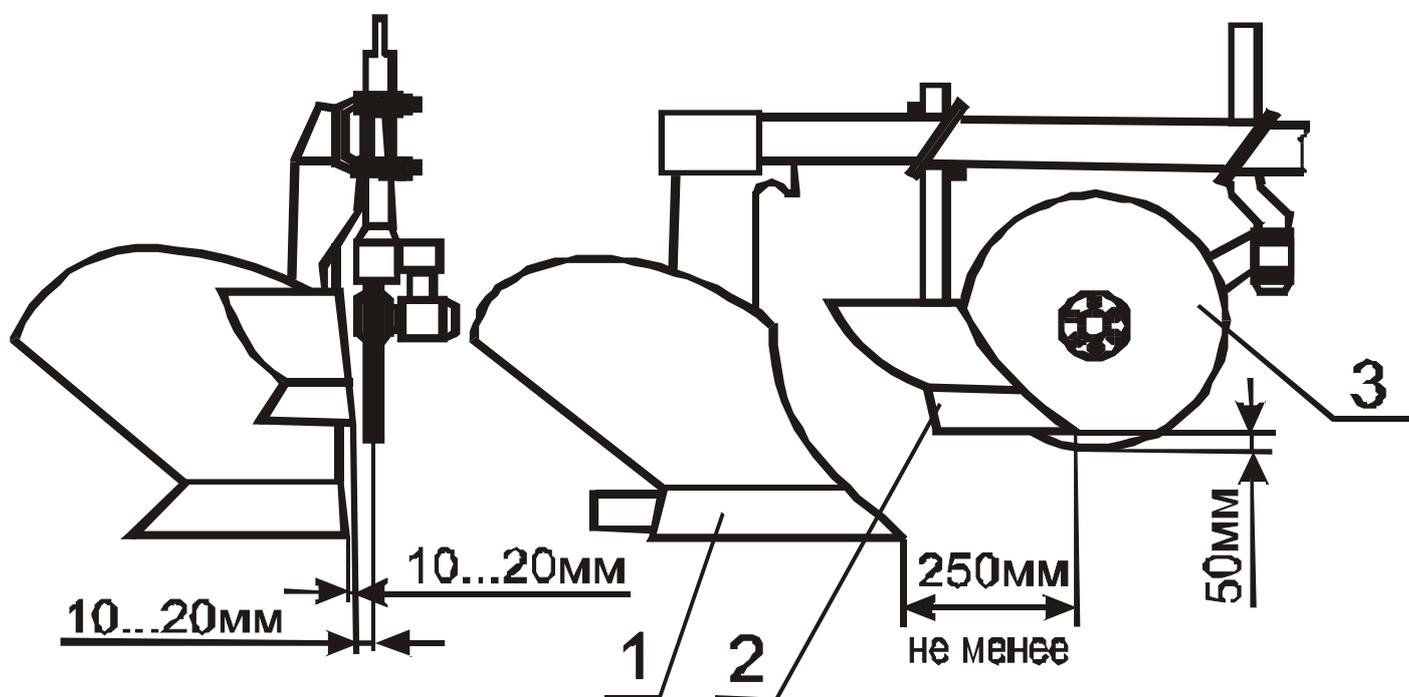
Расположение дискового ножа, корпуса и предплужника
